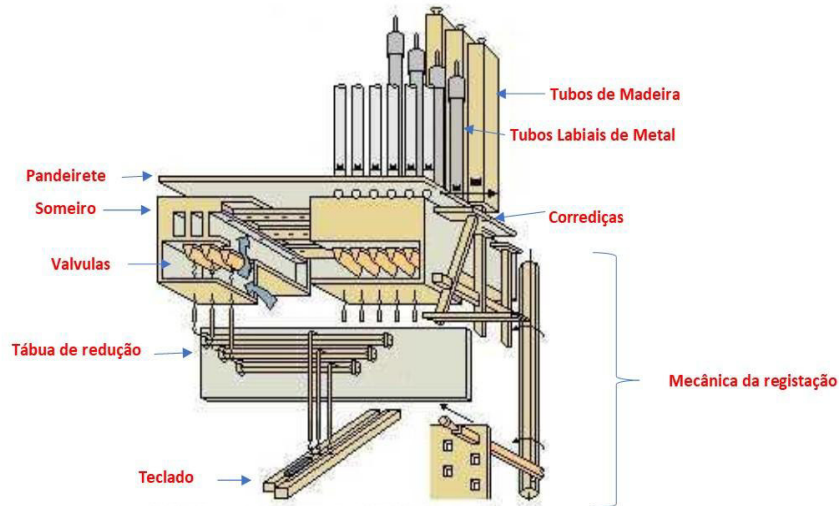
Desenho técnico das partes constituintes principais de um órgão de tubos
